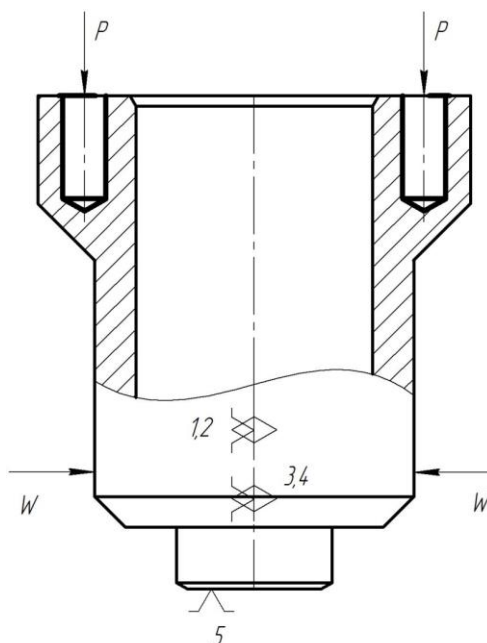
Схема базирования заготовки в приспособлении с указанием мест приложения силы зажима.
